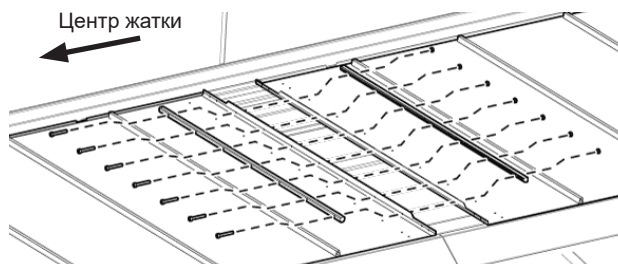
Установка соединительного стержня полотенного транспортера.
